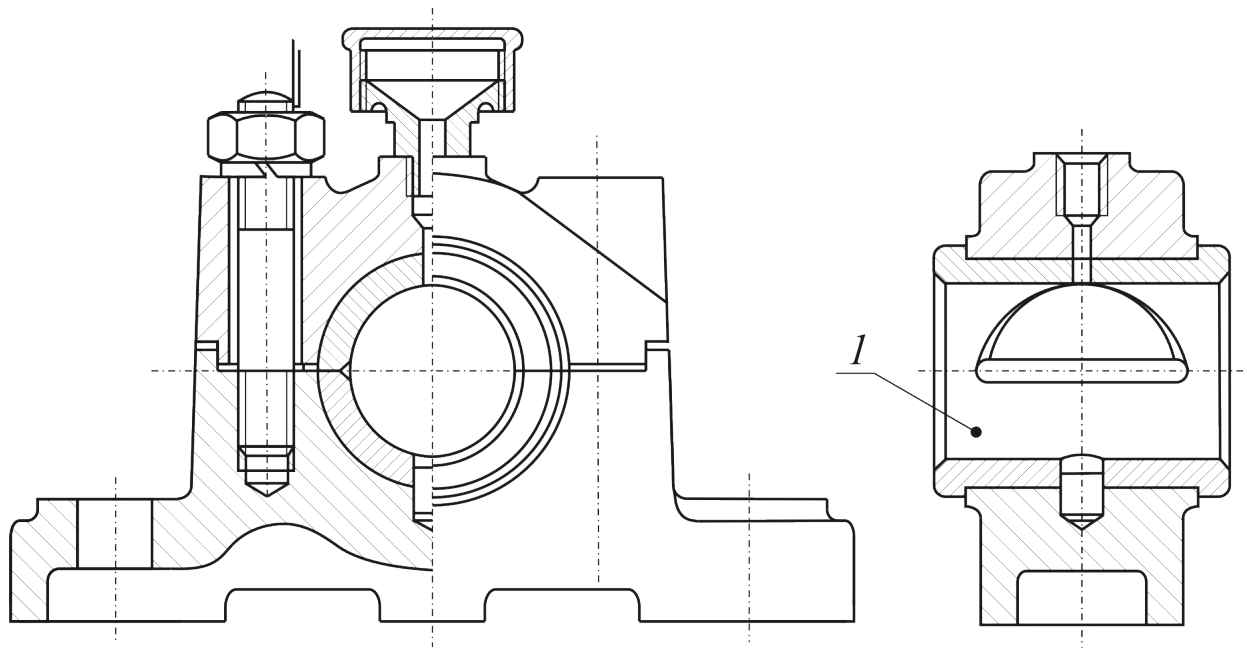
Подшипник с разъемным корпусом и вкладышем (1- вкладыш)
